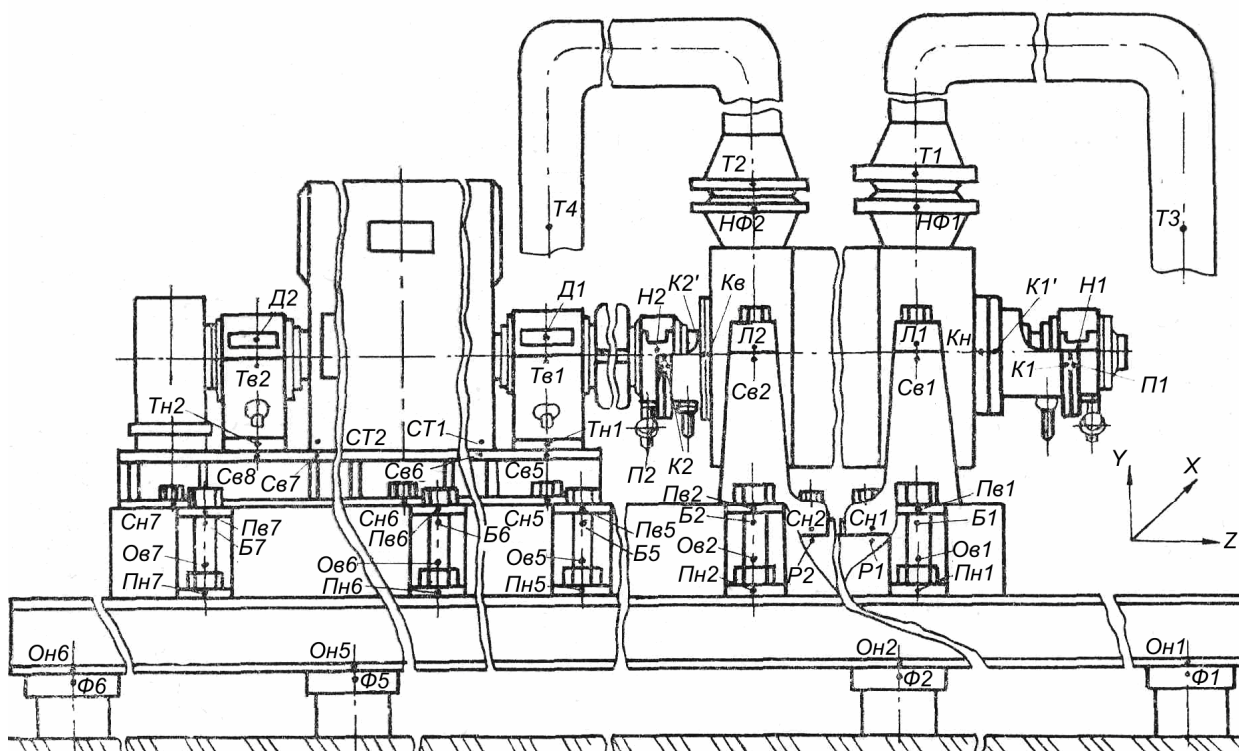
Схема розміщення контрольних точок на корпусі ЦНС-180-1900
